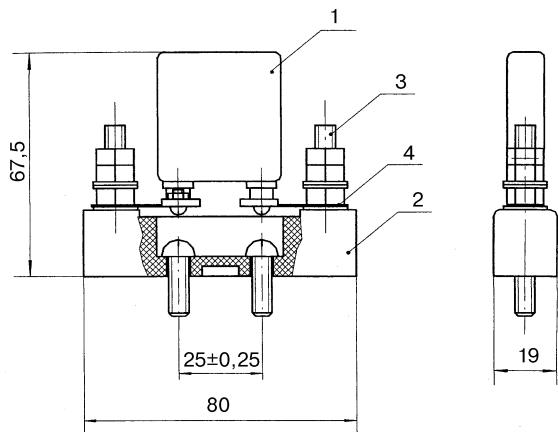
Внешний вид блока Б3П 1-10, где: 1 — варистор; 2 — контактная колодка; 3 — болт; 4 — контакт
